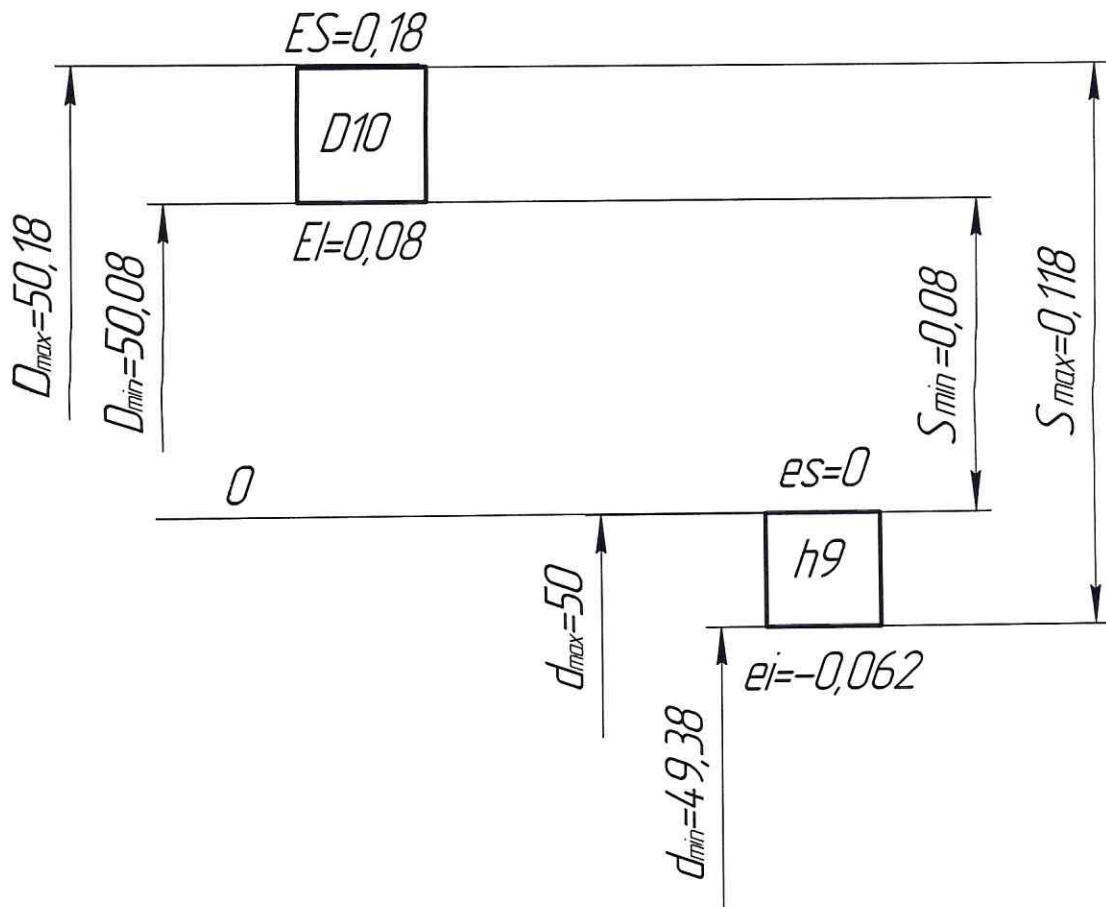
Схема расположения полей допусков отверстия и вала
